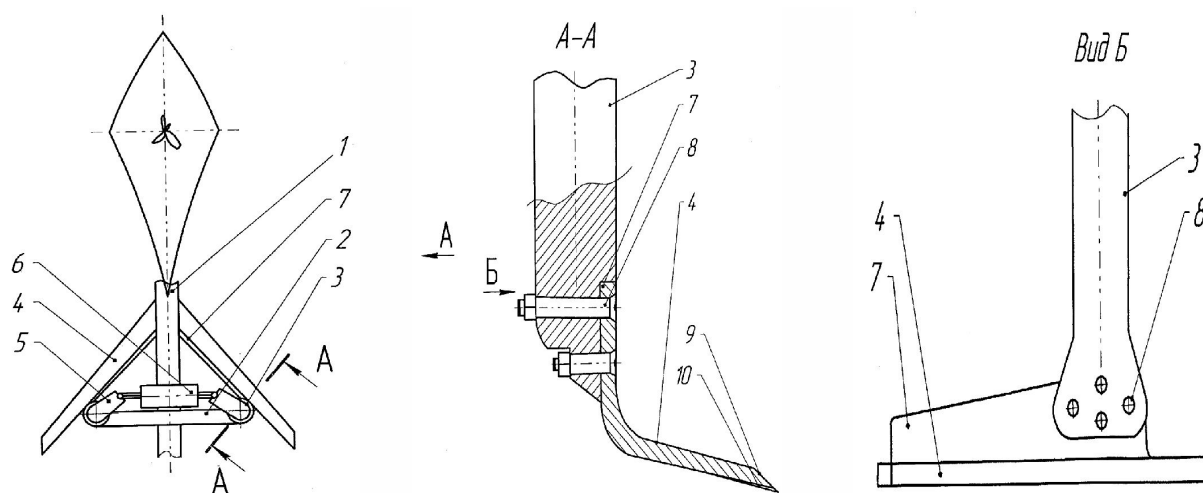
Секция орудия для обработки почвы в рядках: а – грядиль, б – поперечина, в – поворотная стойка, г – поворотная лапа, д – рычаги, е – пневмоцилиндр, ж – щит-отражатель, з – крепежные болты, и – заточка, к – наплавка.
